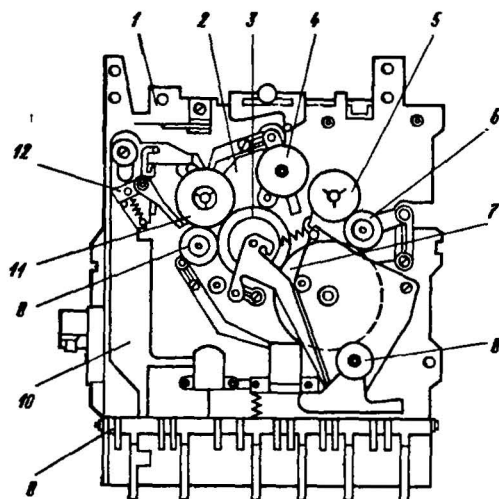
Общий вид ЛПМ (вид сверху):
